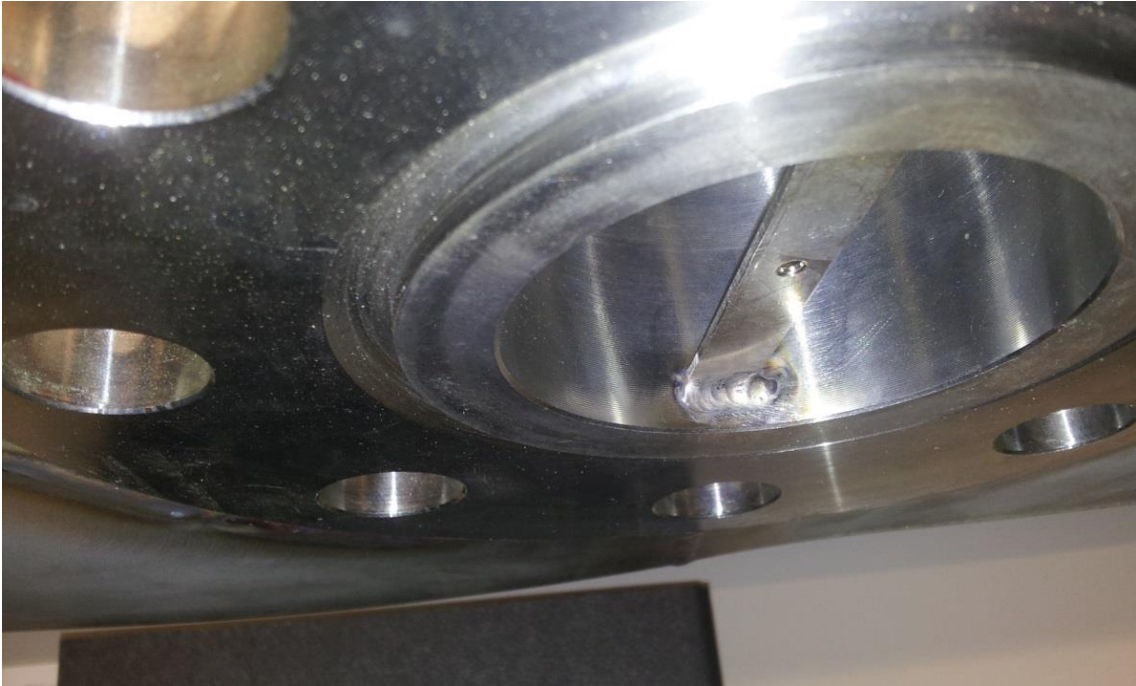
Trapezrührer mit Lagerzapfen)
